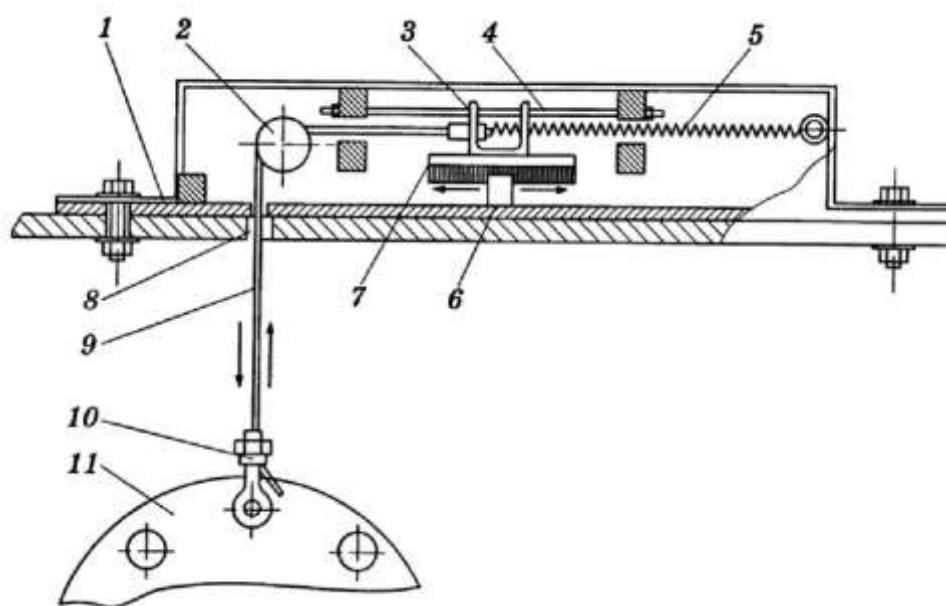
Схема механической части толчкомера ИВП-1М: 1 – корпус; 2 – направляющий ролик; 3 – п-образный механизм; 4 – направляющие штанги; 5 – пружина; 6 – электронная оптопара; 7 – ходовая пластина; 8 – отверстие в полу кузова автомобиля; 9 – трос; 10 – зажимное устройство для закрепления троса; 11 – задний мост автомобиля [собственный материал]
